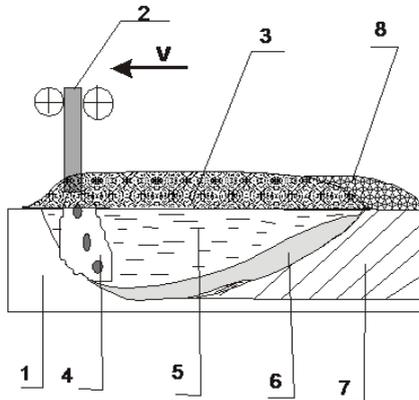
Схема процесса автоматической сварки под слоем флюса:
